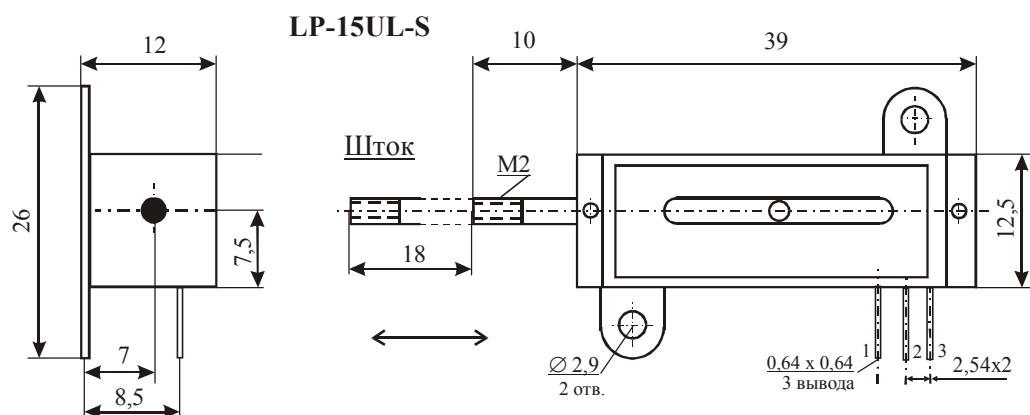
Внешний вид и габаритные размеры датчиков линейных перемещений типа LP-15UL-S
